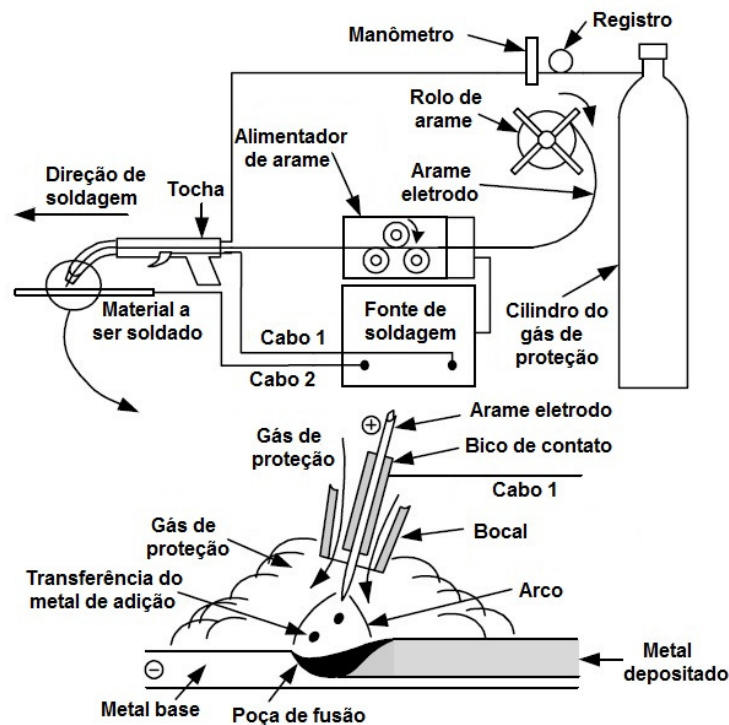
Desenho esquemático do processo de soldagem MIG/MAG.
